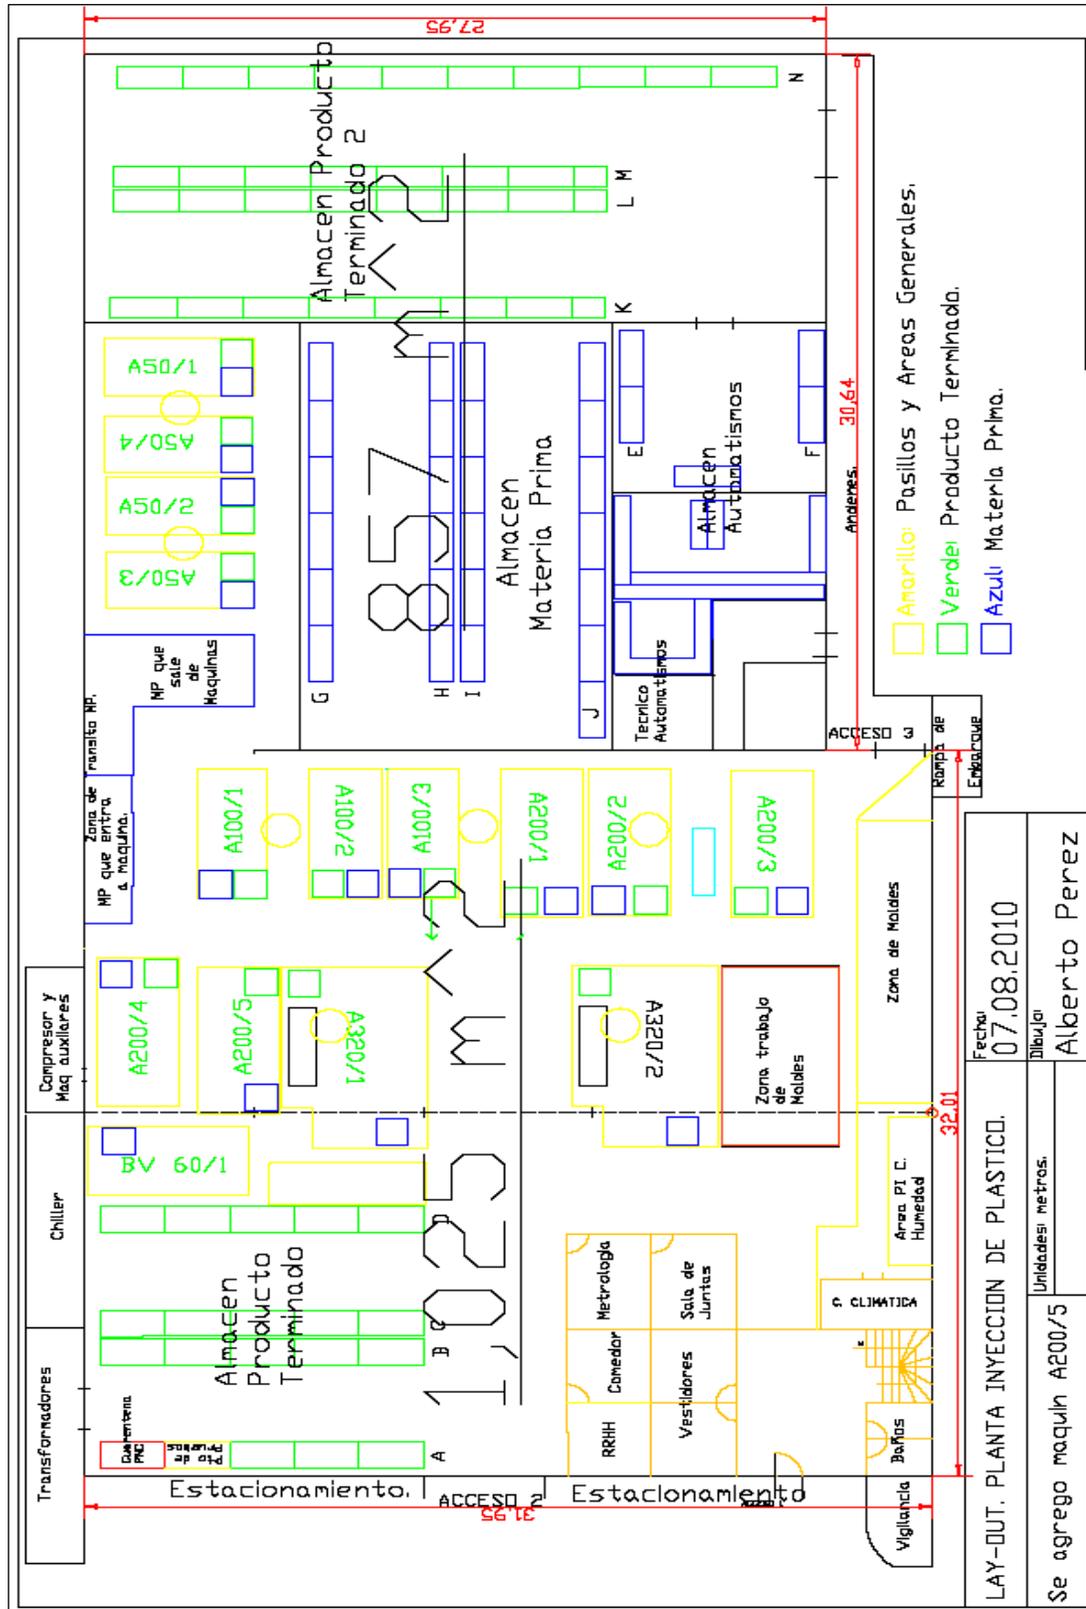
Distribución de planta actual. Fuente: Elaboración propia.
